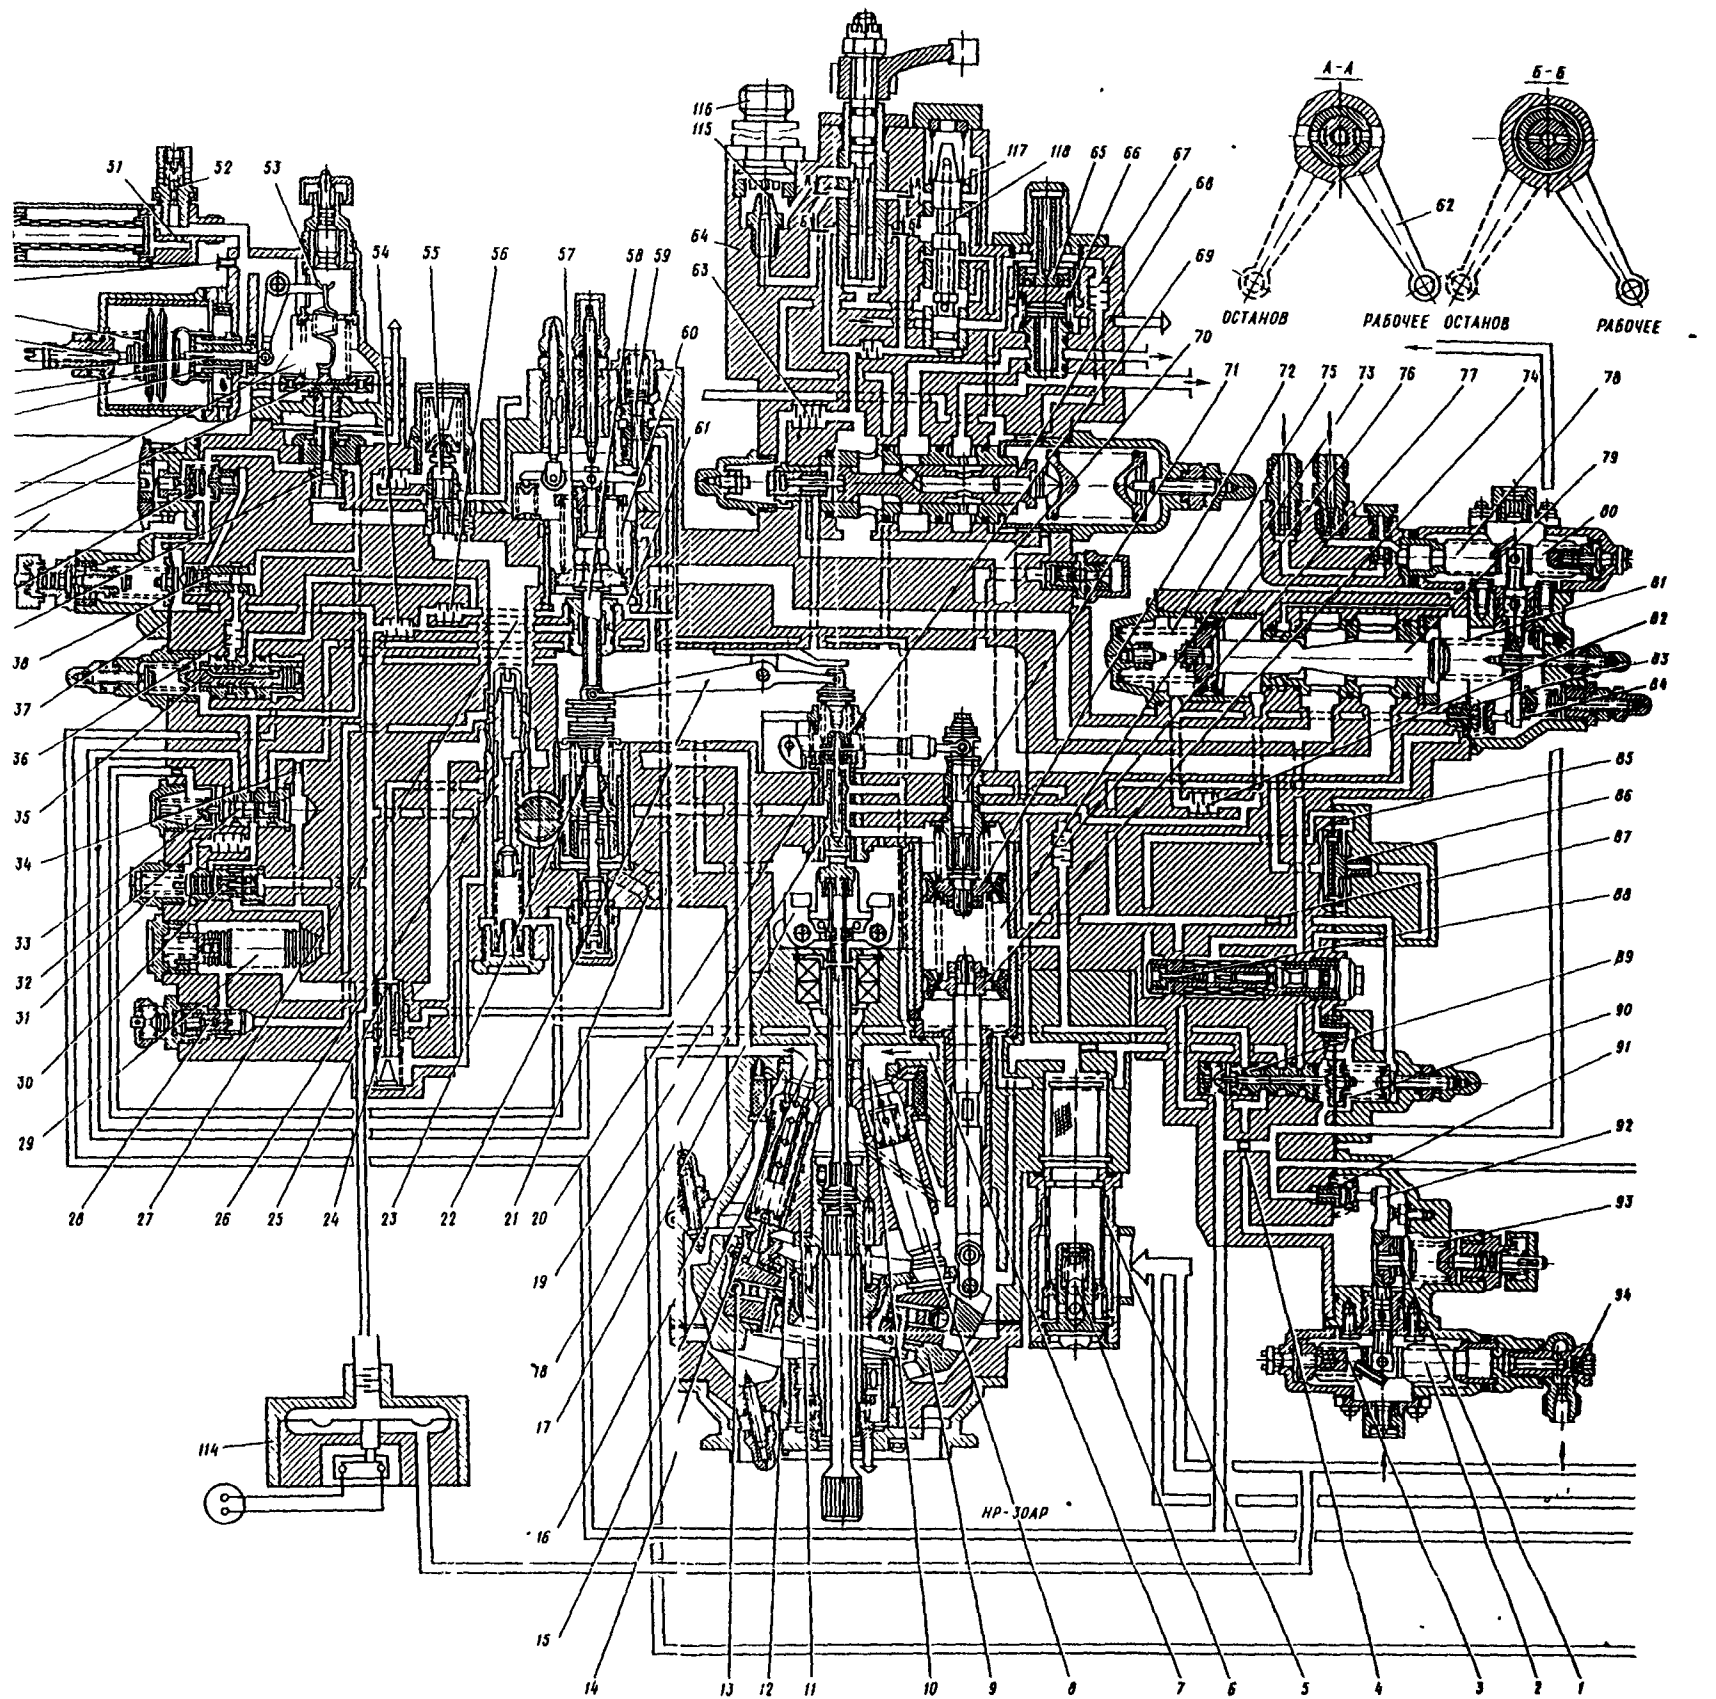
(Лист 1) Схема топливной автоматики двигателя:
